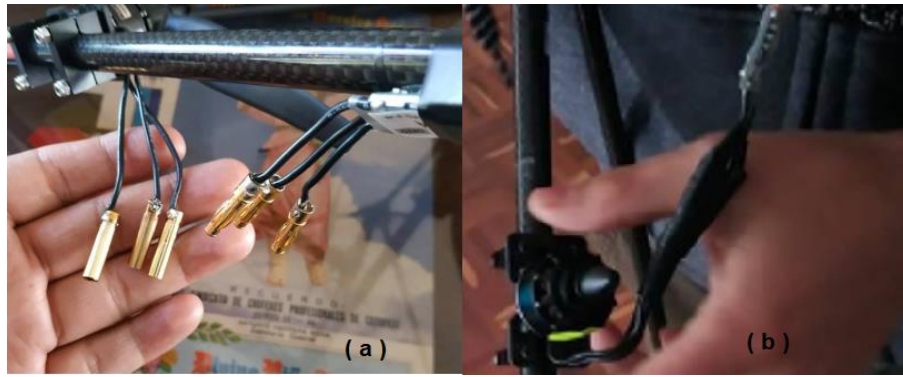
a). Soldadura de conectores b) Aislamiento de uniones.
